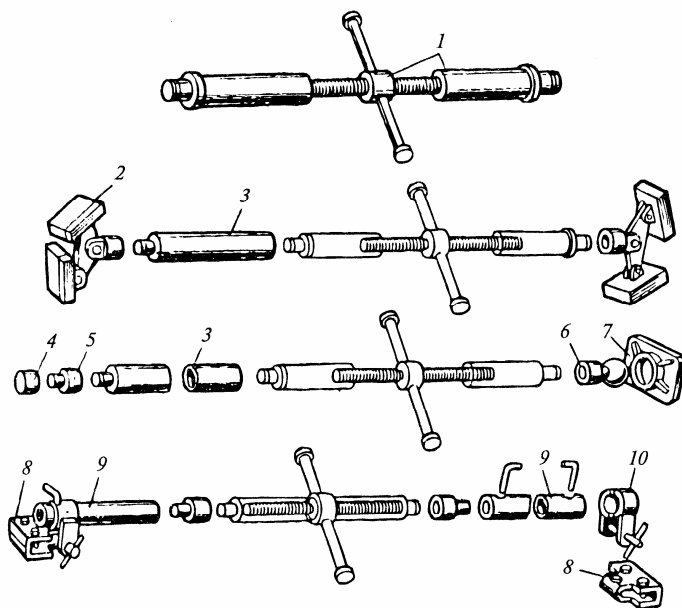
Комплект винтовых растяжек: 1 – винтовая растяжка; 2 – шарнирные упоры; 3 – удлинители; 4 – цилиндрический упор; 5 – переходник; 6 – сферический упор; 7 – опорная пята; 8 – струбцина; 9 – проставка; 10 – угловой переходник
